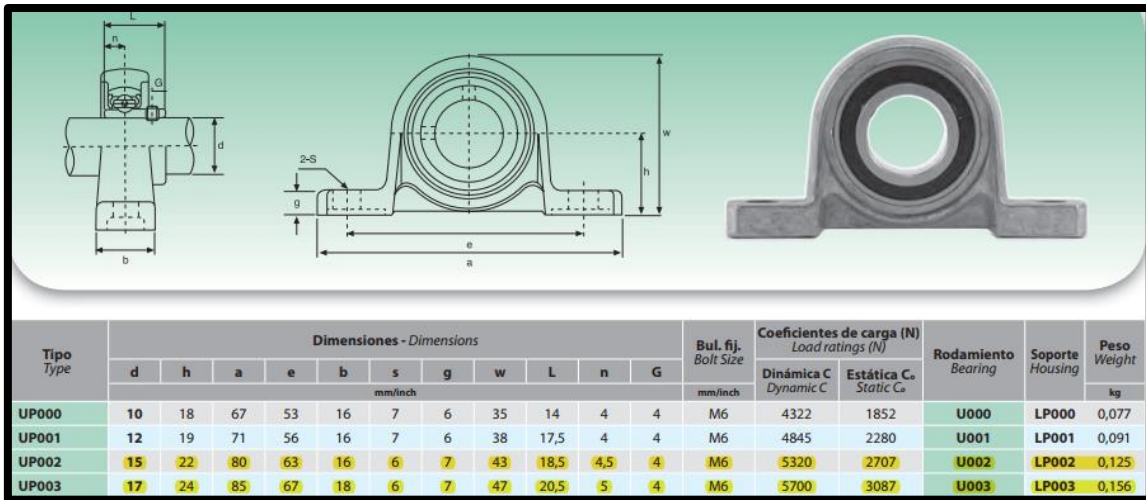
Rodamientos con soporte seleccionados de 15 y 17 mm. Fuente: Catálogo Rodamientos ISB.
